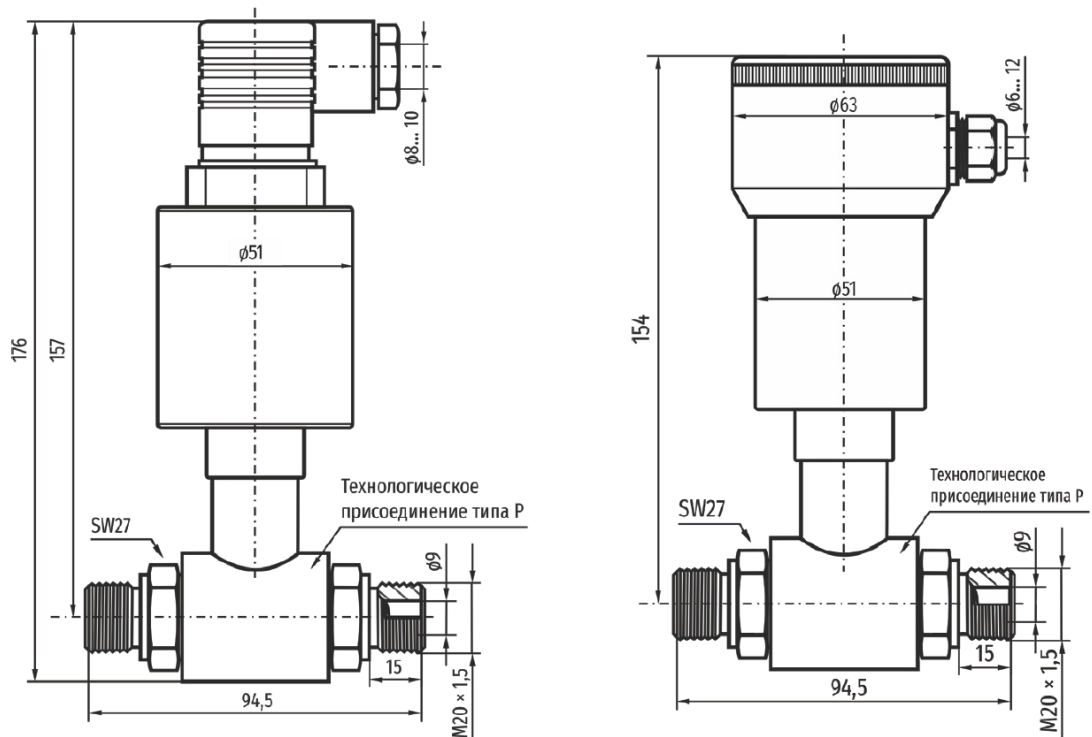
Преобразователь давления измерительный APR-2000 с типом процессного присоединения Р. Внешний вид и габаритные размеры
